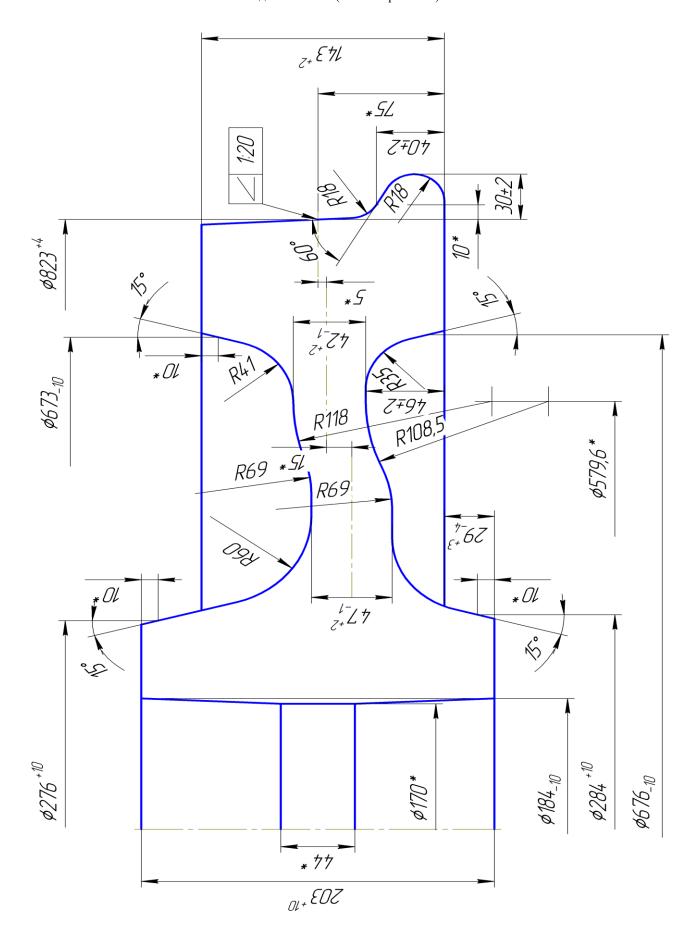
Колесо с черновой механической обработкой (после 1 MO) \varnothing 823 мм. под чистовое \varnothing 813 мм, чертеж №КР-0017-16. Масса колеса - 427кг.
